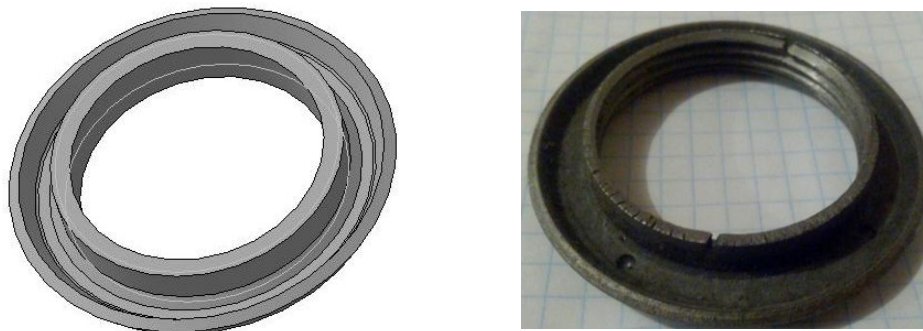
Загальний вигляд та типові дефекти деталі "Втулка"
